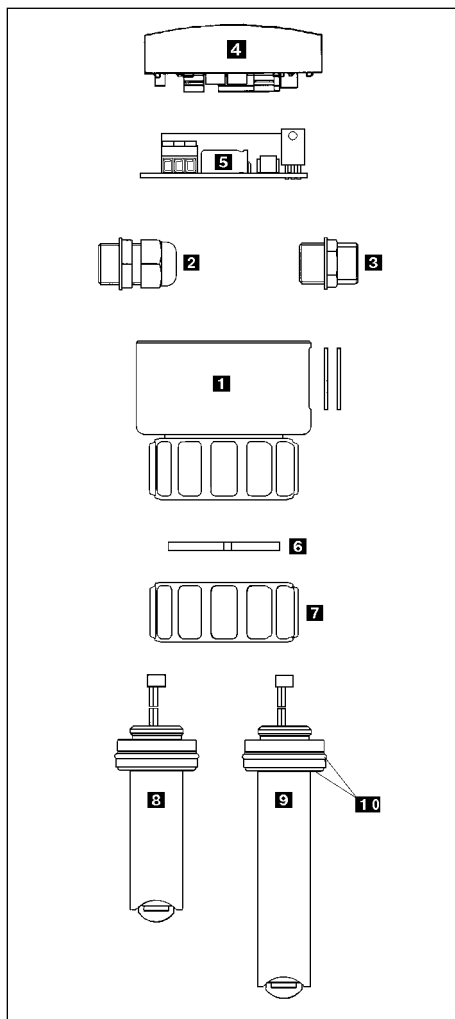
Vue éclatée des pièces de rechange 8025 version compacte
